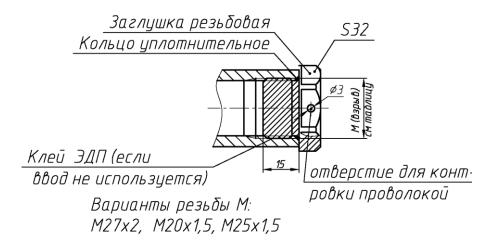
Элементы взрывозащиты при поставке табло с резьбовыми заглушками
